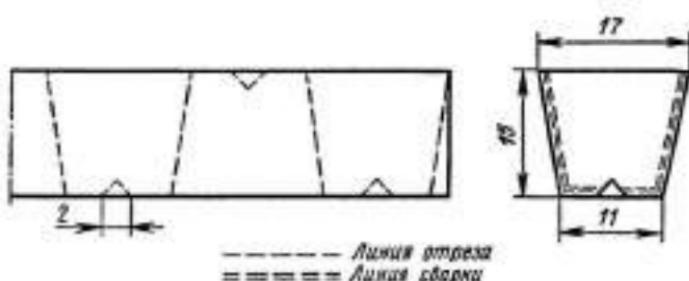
Схема нарезки горшочков из полистиреновой пленки (пунктиром показана линия отреза, двойным пунктиром — линия сварки)
